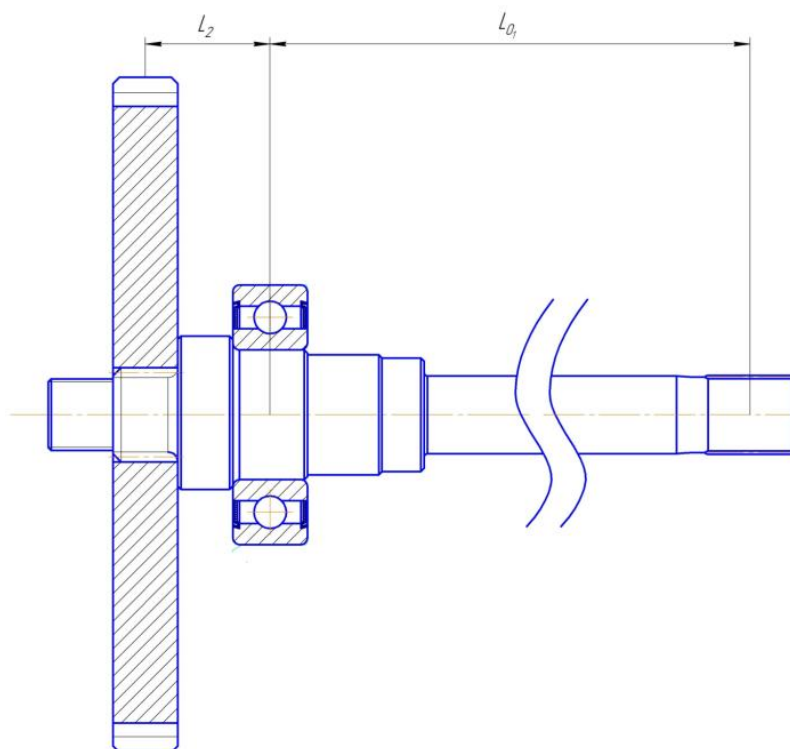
Компоновка ведущего вала заднего колесного редуктора
